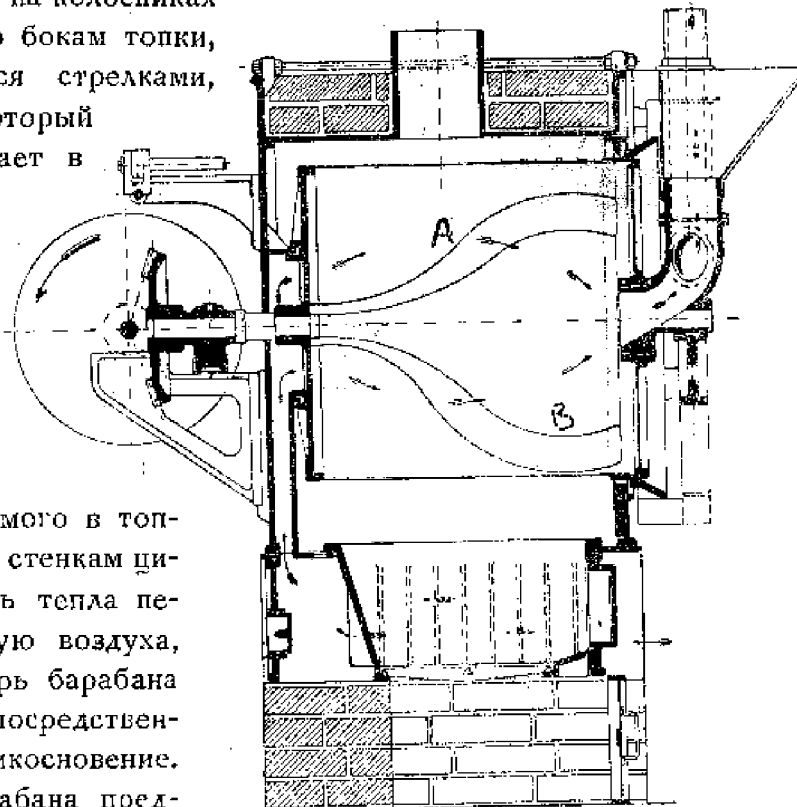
Цилиндрический обжарочный барабан. Продольный разрез.
